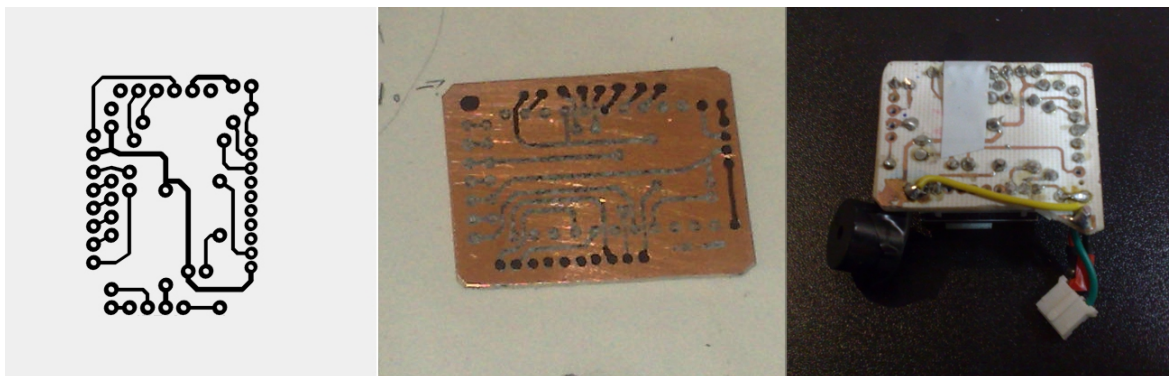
processo de fabrico da PCI e montagem. Ao lado esquerdo está representado o desenho do circuito físico, o qual foi transferido por via térmica para uma placa de cobre, visível na imagem ao centro. Do lado direito podemos observar os vários componentes soldados e montados na PCI.
